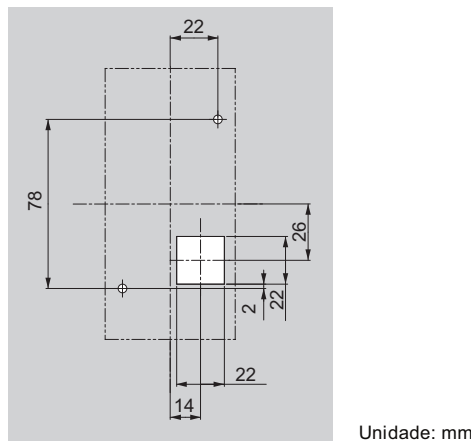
Dimensões de corte do painel (instalação de montagem externa/na superfície)
